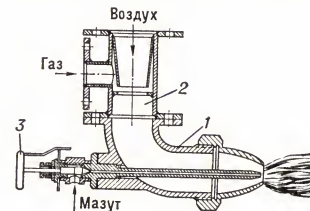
Комбинированная газо-мазутная горелка: 1 — корпус горелки; 2 — камера смешения; 3 — регулятор подачи мазута.
